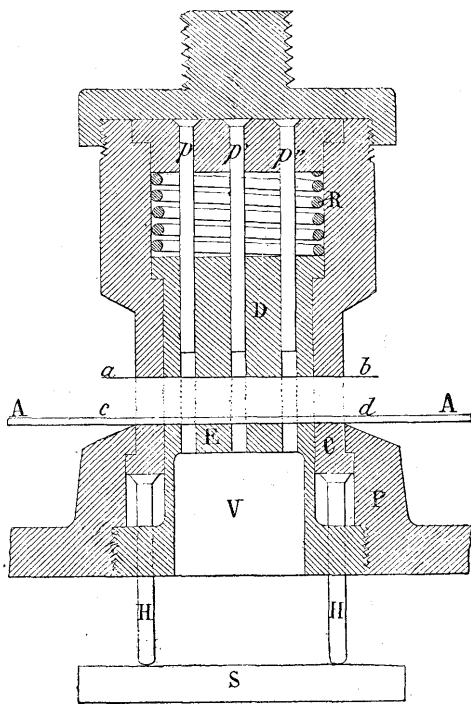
Presse à découper, à emboutir et à ajourer, de MM. Lapipe et Wittmann, de Paris.
